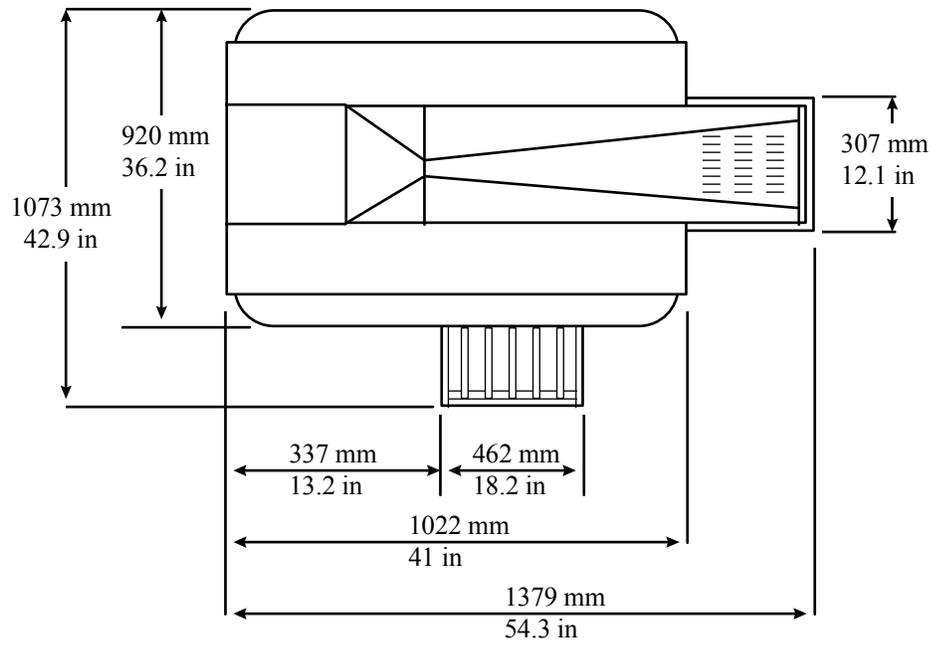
Dimensions SOLO™ XL (Vue de dessus)
